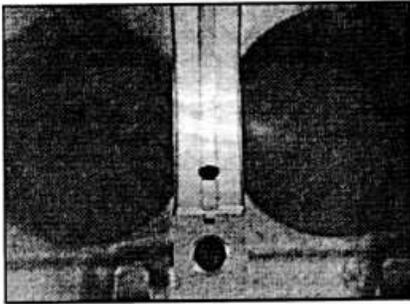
D.74. Выступ на каждом коренном вкладыше должен совмещаться с пазом в блоке цилиндров, а отверстия для подачи смазки должны совместиться с масляными каналами блока цилиндров.
